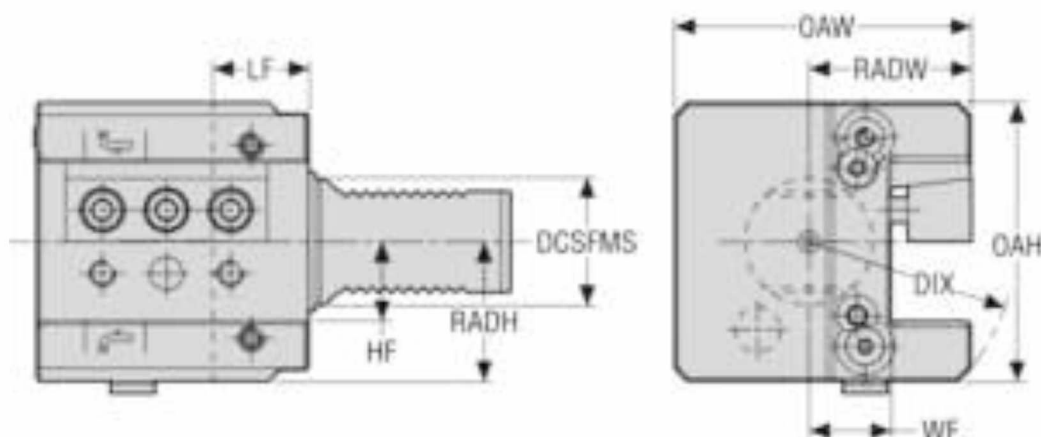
Допоміжний інструмент ASHN-VDI40-25-JETI [2]
